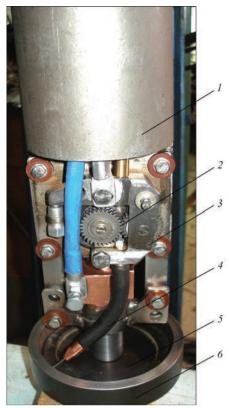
Сварочная часть аппарата для глубоководной сварки: 1 — корпус; 2 — механизм подачи; 3 — механизм колебаний; 4 — сварочная горелка; 5 — заглушка; 6 — фрагмент трубы
